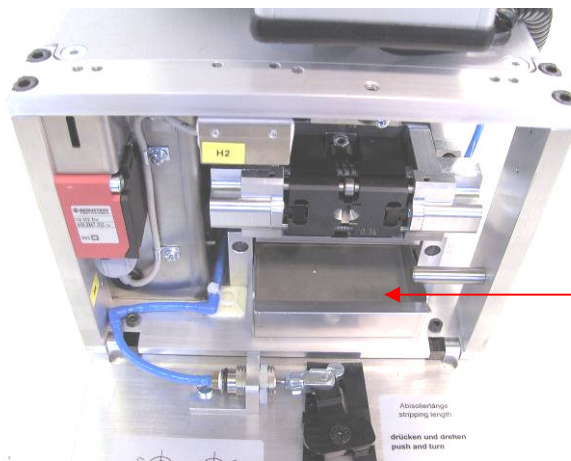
Crimpwerkzeug / Crimping tool
